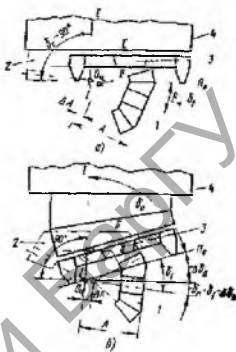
Обработка конических зубчатых колес с круговой линией зуба по схеме плосковершинного (а) и конусного (б) производящего колеса
